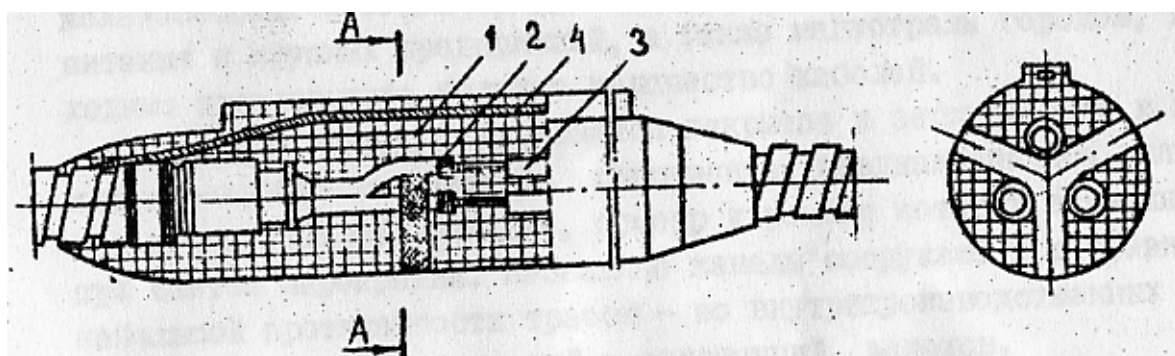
Соединительная муфта: 1 – корпус муфты; 2 – распорка; 3 – соединительная гильза; 4 – провод заземления
